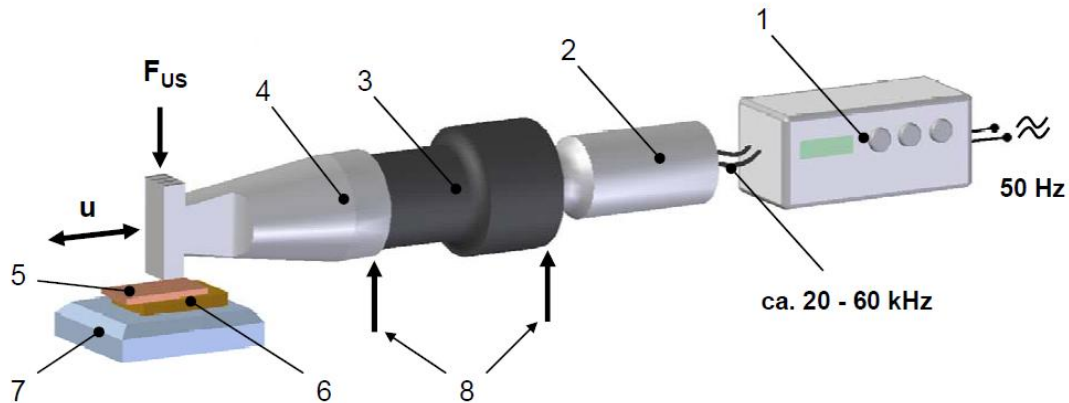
Prinzipieller Aufbau einer Ultraschallschweißanlage [15,18]
